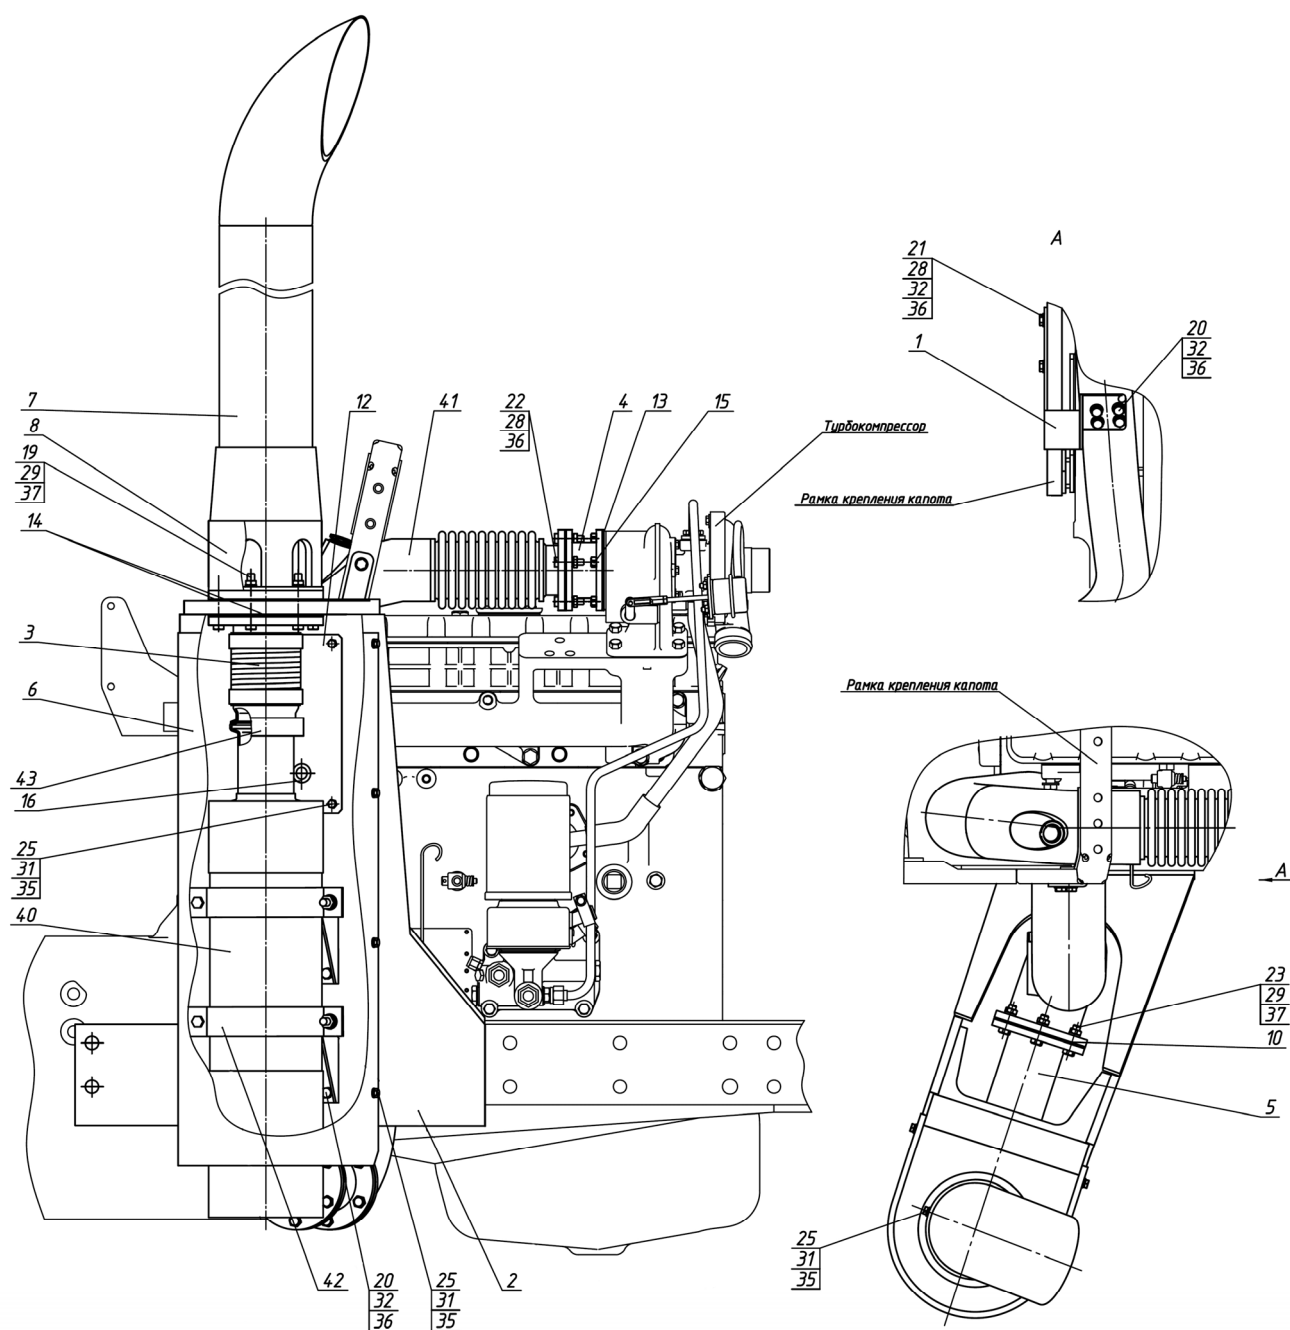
Установка глушителя (1220.5P-1205005/-A)
